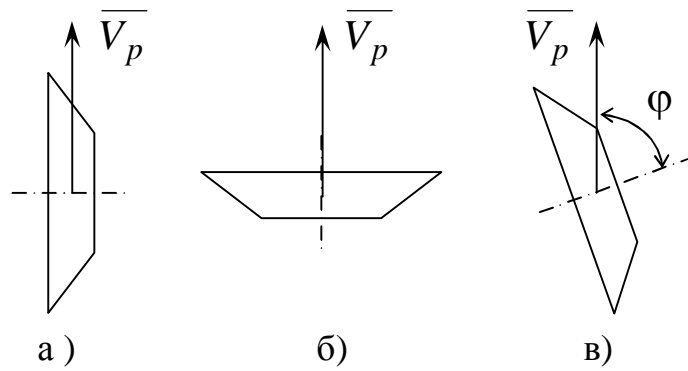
Схемы установки режущего инструмента с вращающейся режущей кромкой.
